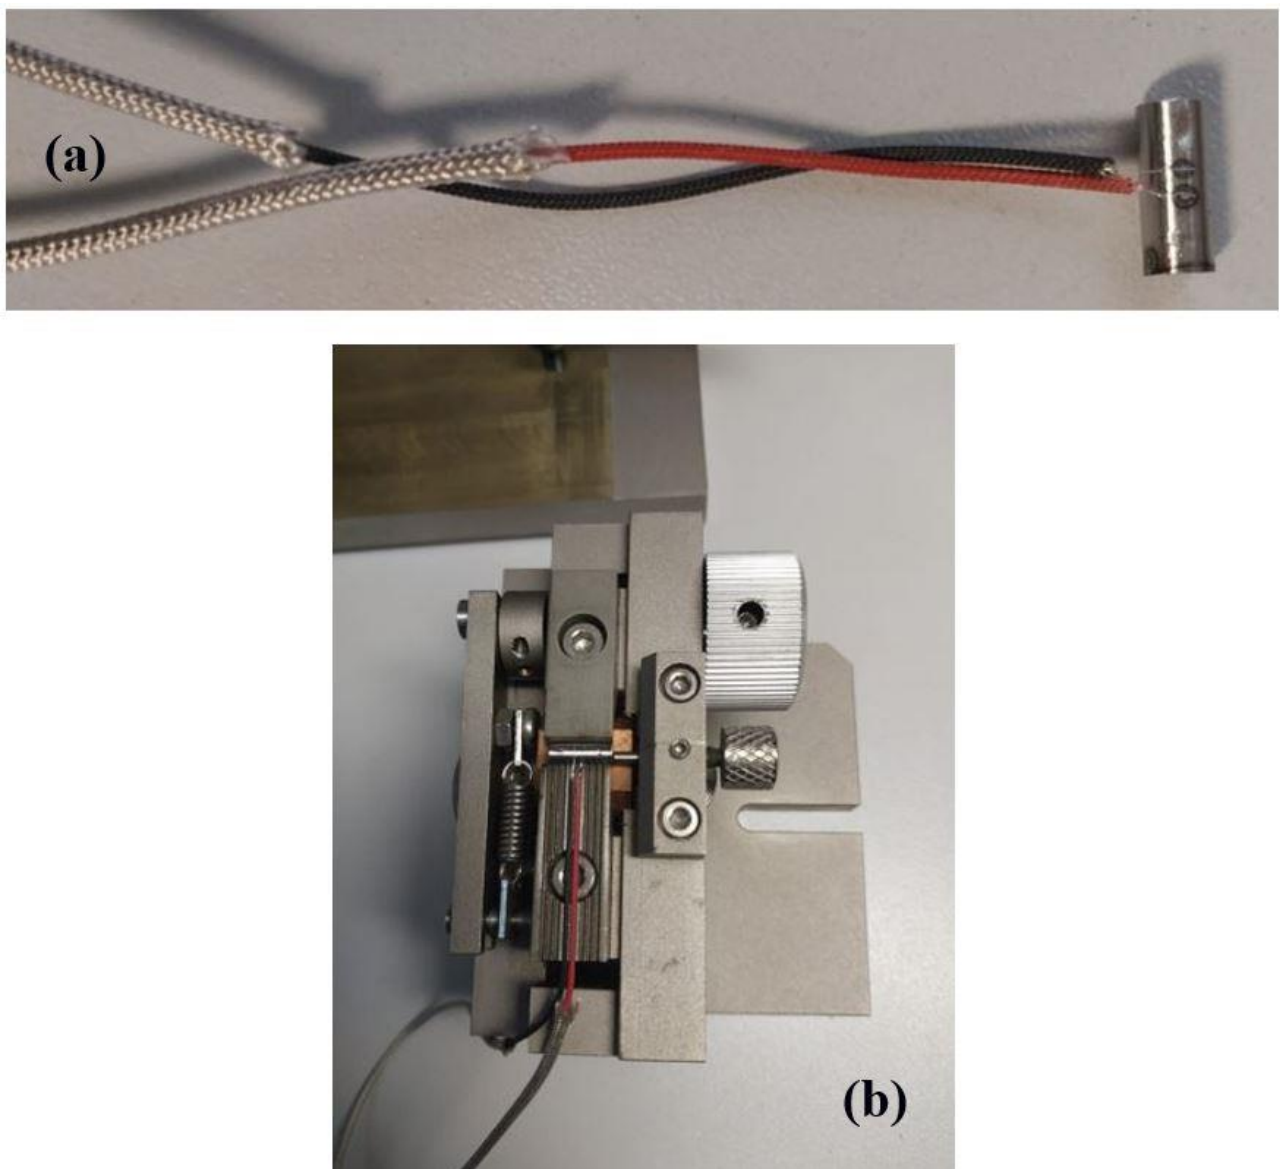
(a) Probeta de Zry-4 con termocupla soldada (b) Soldadora de punto del equipo.
